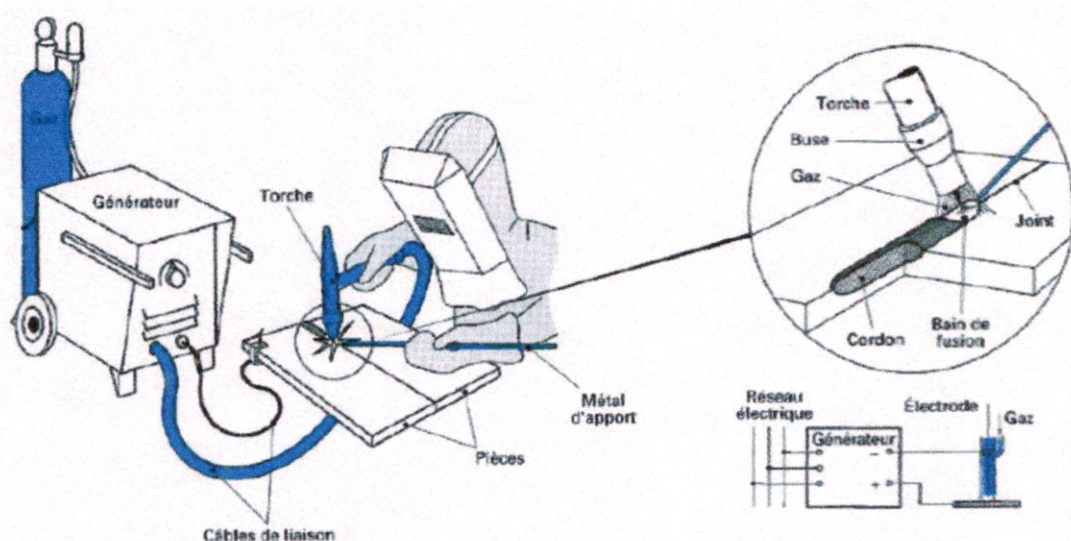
Soudage à l'électrode réfractaire : principe.
